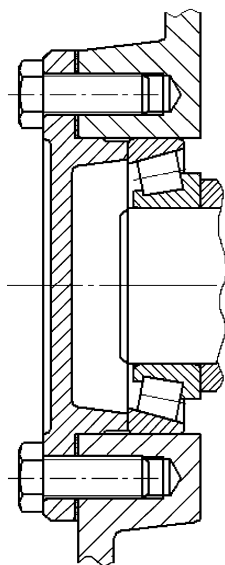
Крепление крышки подшипника к корпусу редуктора
